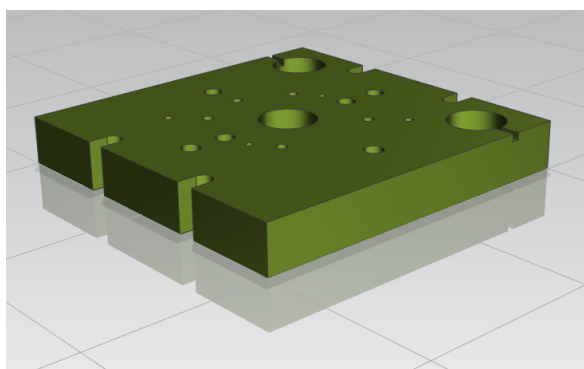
Деталь «Плита верхняя» – Overplate.prt
